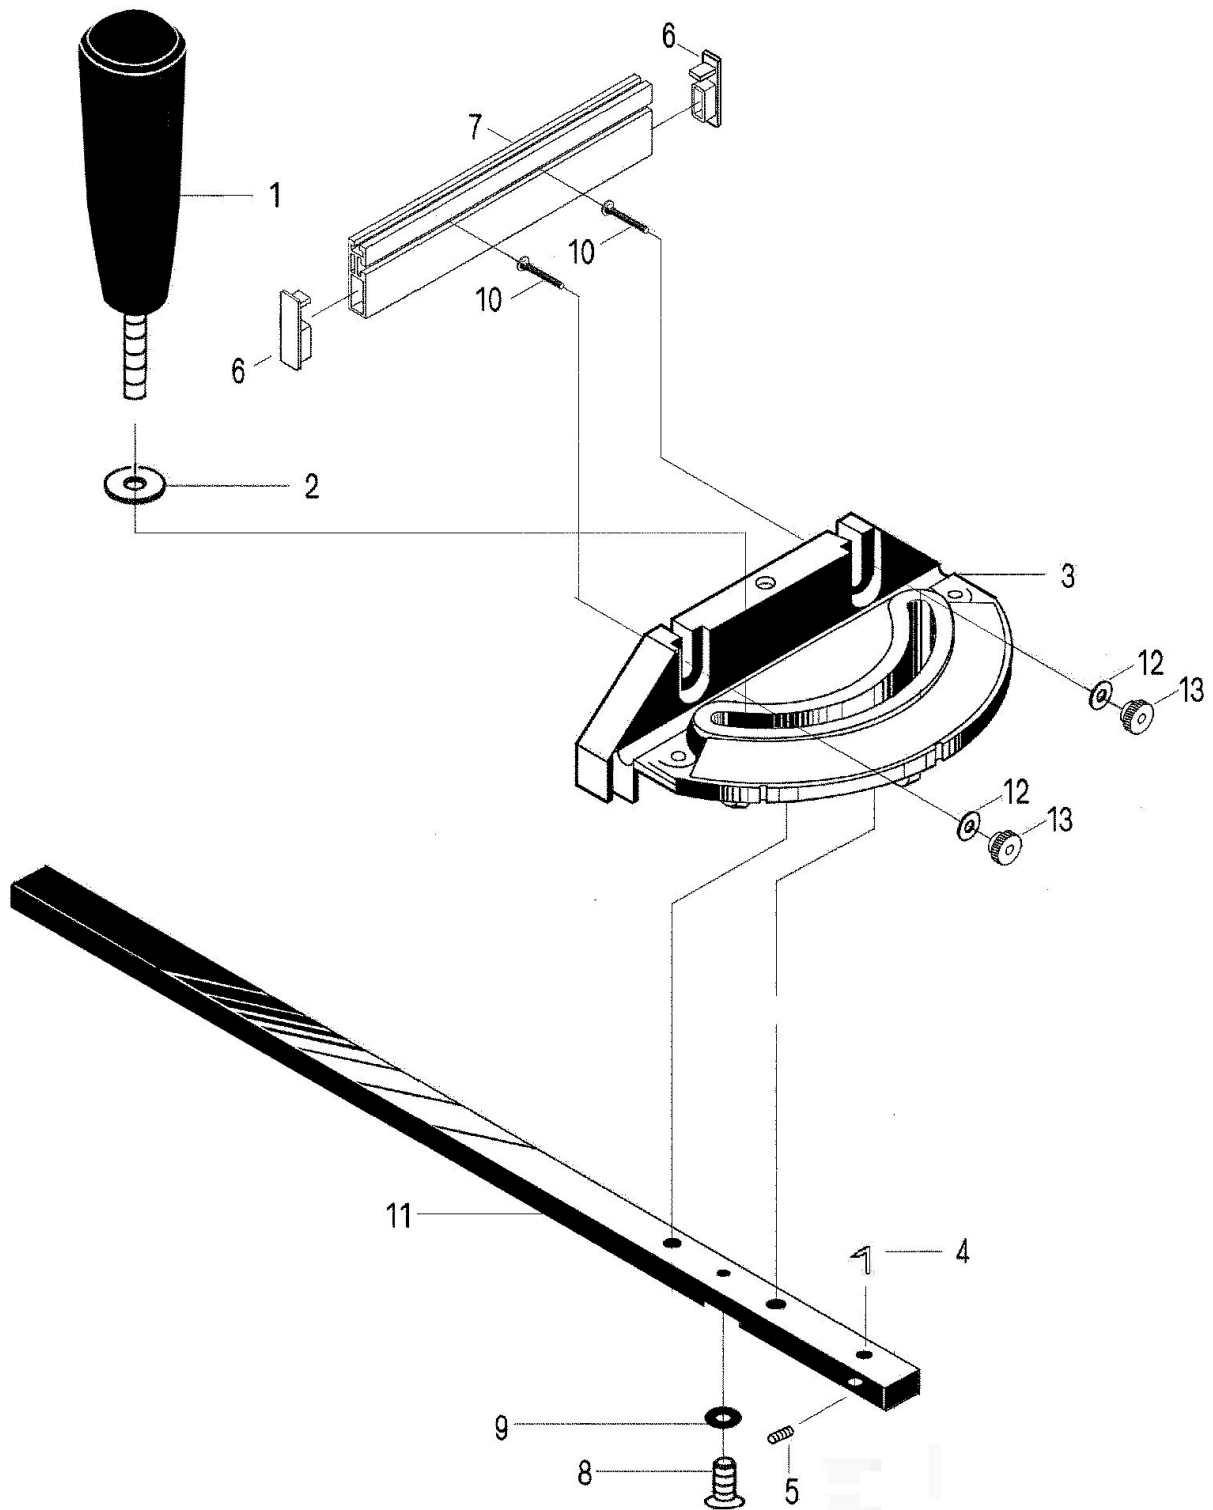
Dessin des pièces détachées 8 - Scie à format FKS 315-2000 E
